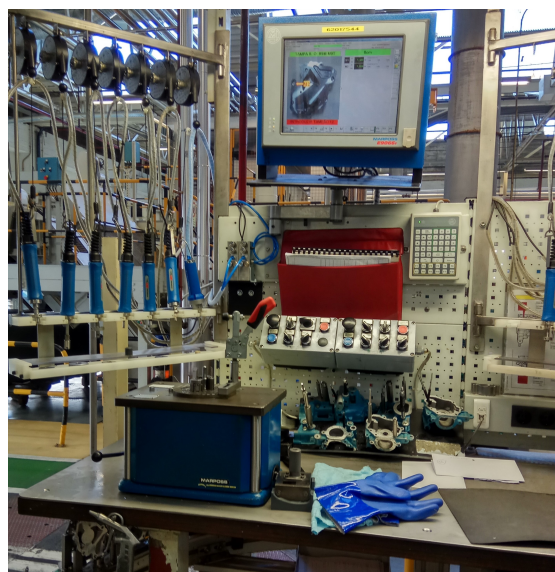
Posto de controlo dimensional Bord de Ligne
